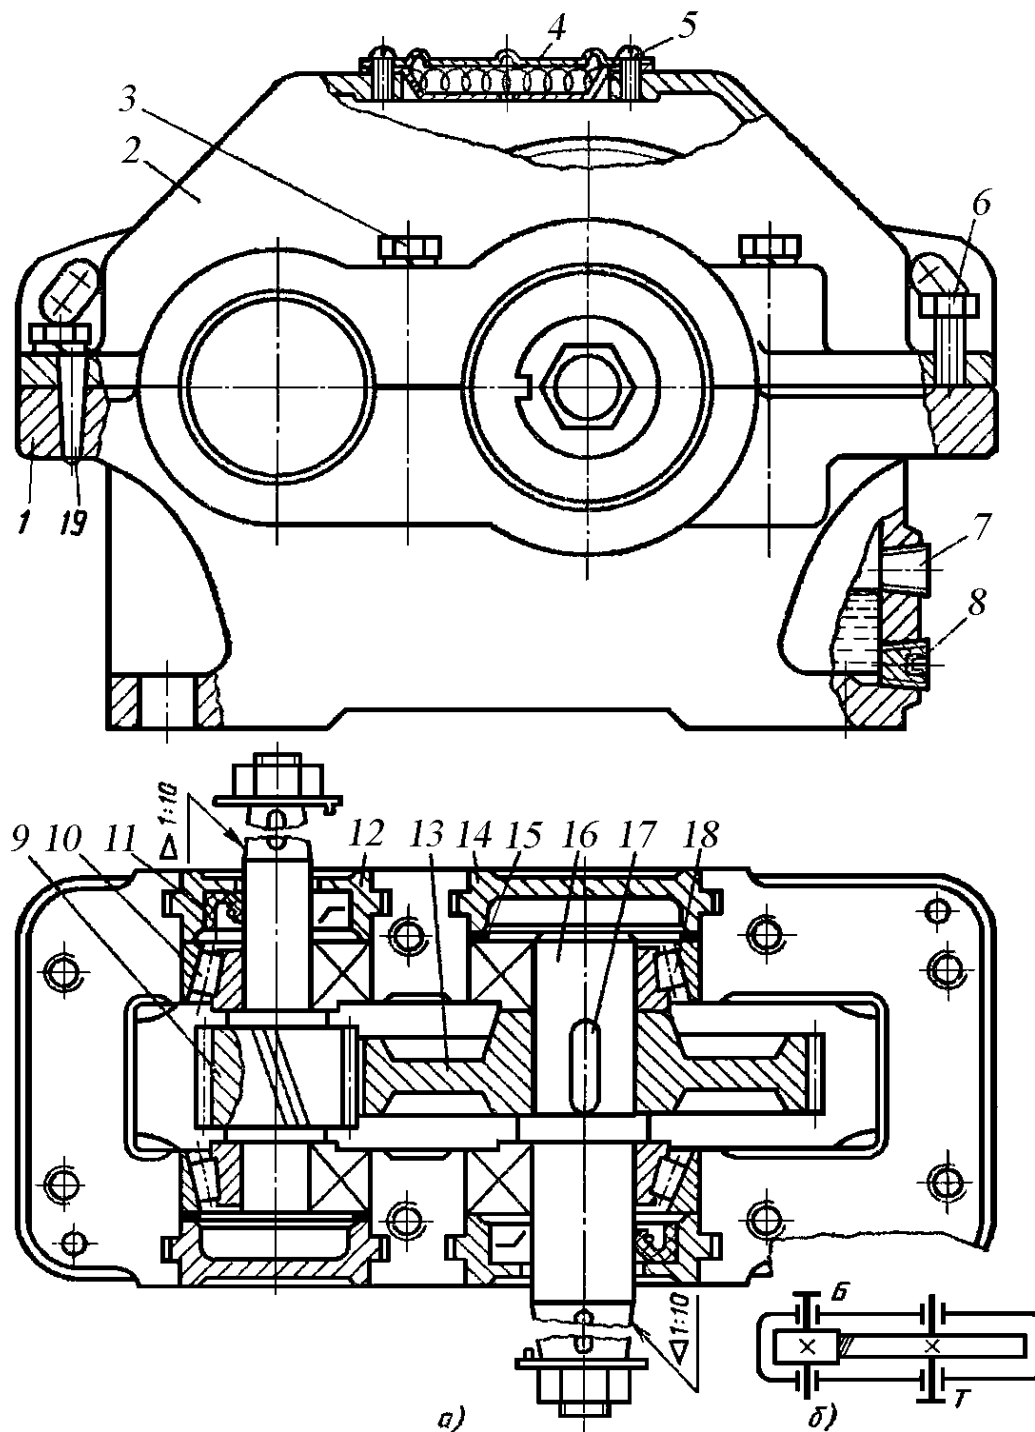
Конструкция одноступенчатого цилиндрического редуктора
